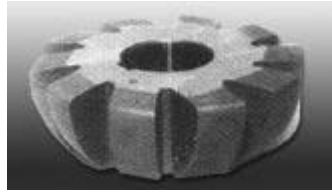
Involute Spur Gear Milling Cutters
